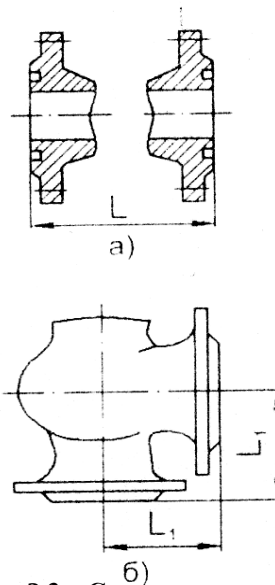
Строительная длина L и L_1 проходной арматуры
